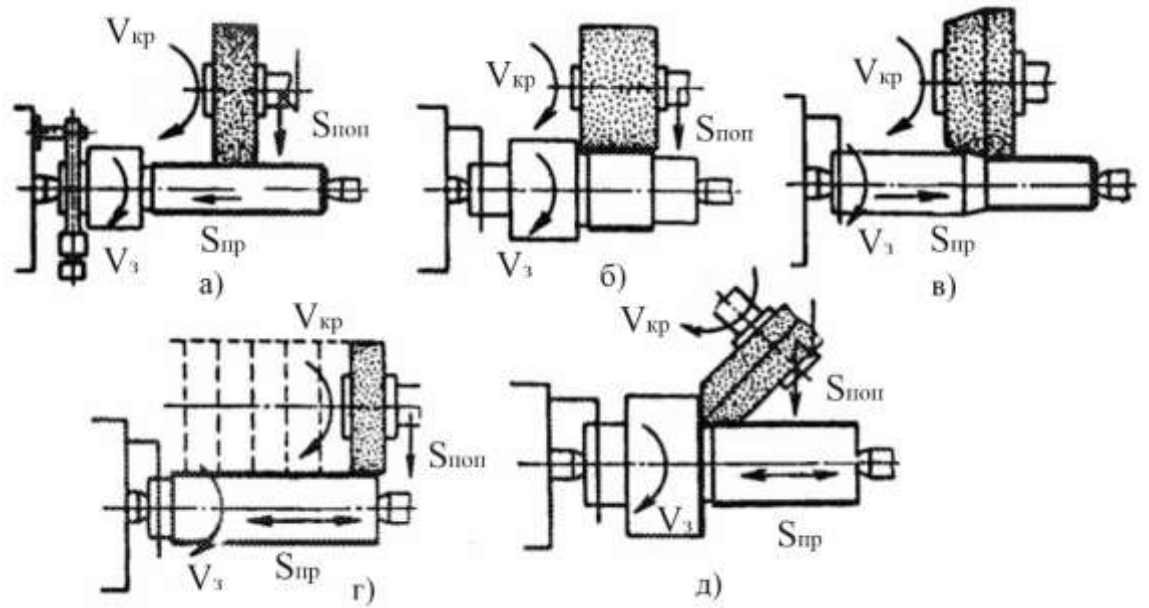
Схеми шліфування в центрах при обробці зовнішніх циліндричних поверхонь: а-з поздовжньою подачею; б - з поперечною подачею (врізне шліфування); в,д - з поздовжньою подачею фасонного кола з одночасною обробкою торця.
